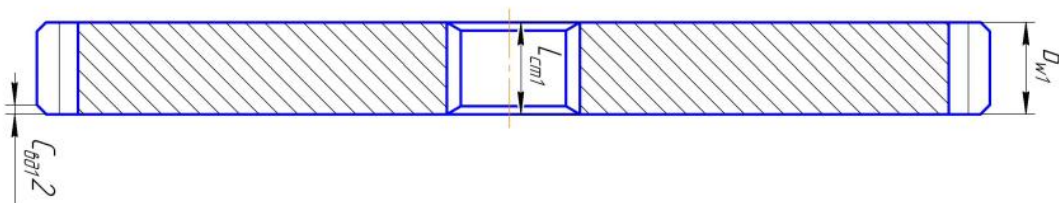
Ведущая шестерня заднего колесного редуктора
